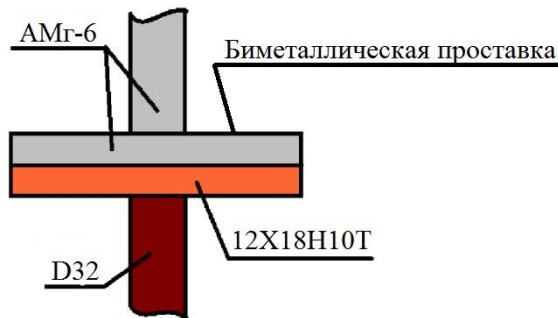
Схема выполнения сварного соединения элементов базовой технологии
